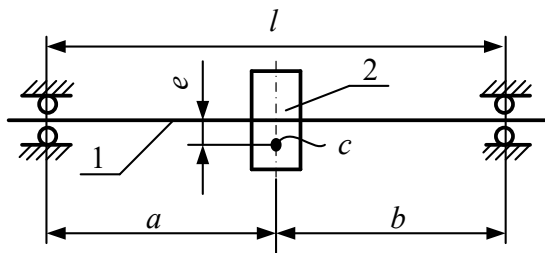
Схема двухопорного вала с диском посередине:
